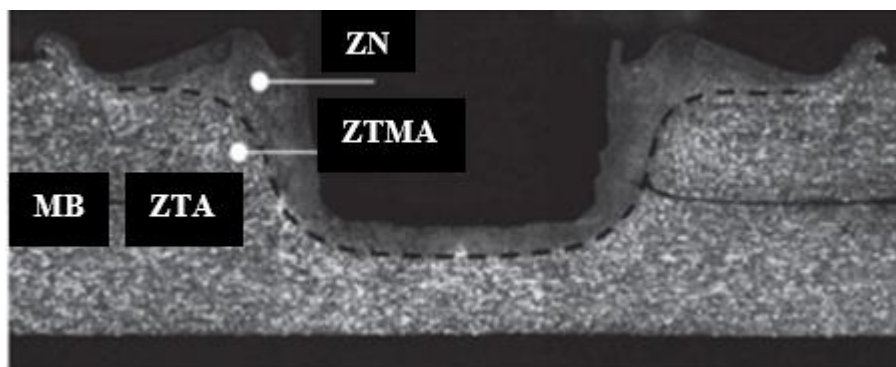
Zonas de soldadura (Campanelli, L. C., *et al.*, 2012).
